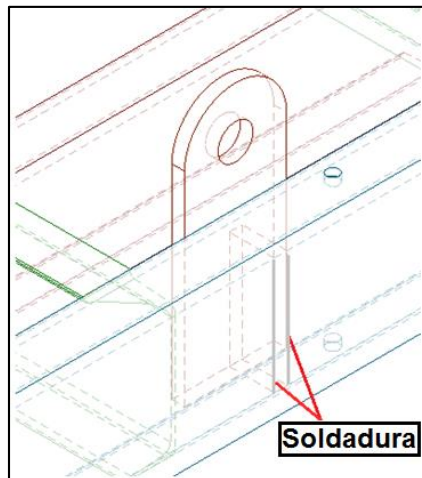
11 Detalle de la unión mediante soldadura entre la oreja de izaje y la viga UNP 300
